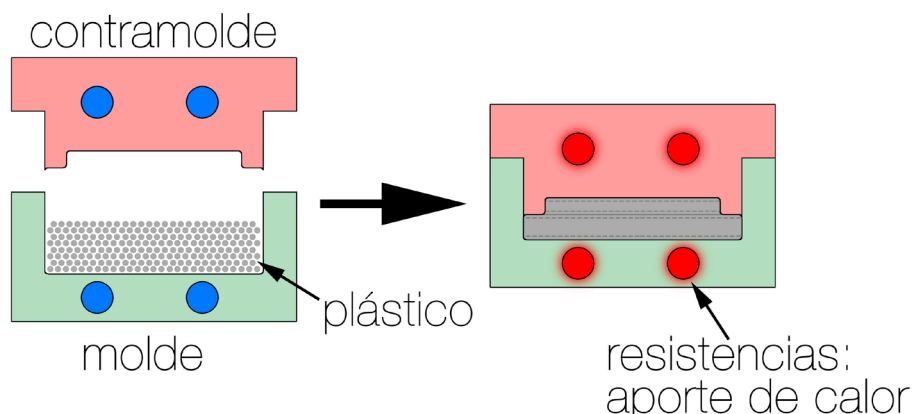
moldeo por compresión pieza "8.2.- Goma pata"
